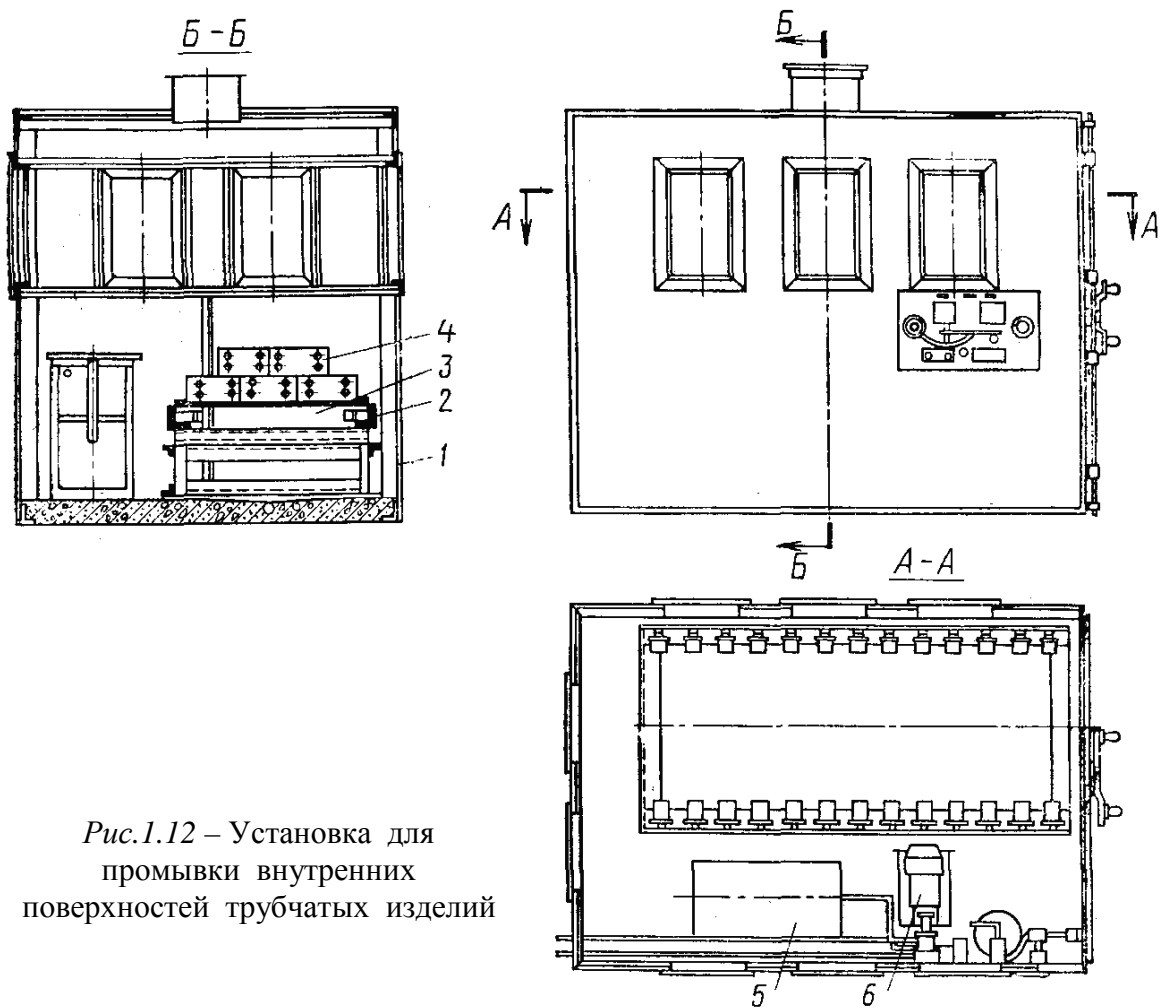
Установка для промывки внутренних поверхностей трубчатых изделий
